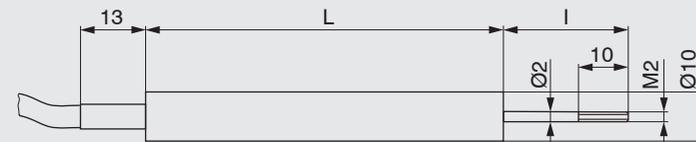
Wegsensor Typ - CA mit integriertem Kabel
